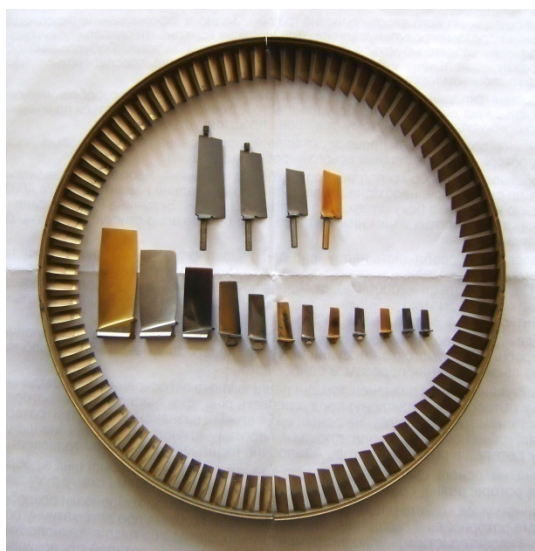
Общий вид лопаток компрессора ГТД модели ТВ3-117
